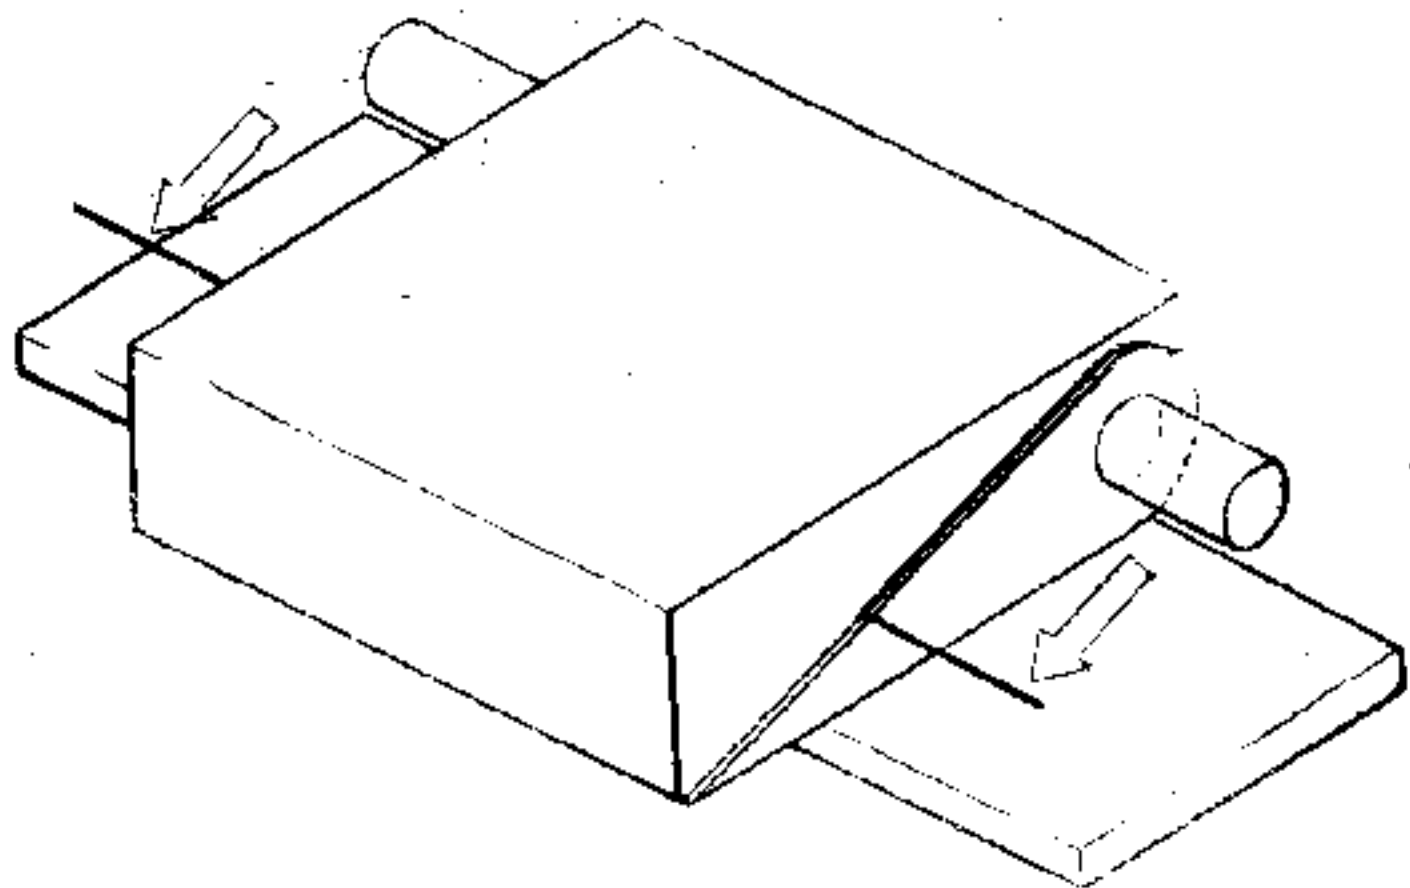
Изготовление блоков наполнителя для рулевых поверхностей.
